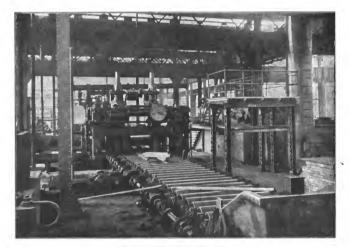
Blechwalzwerksanlage der Bethlehem Steel Co., Bethlehem, Pa.
